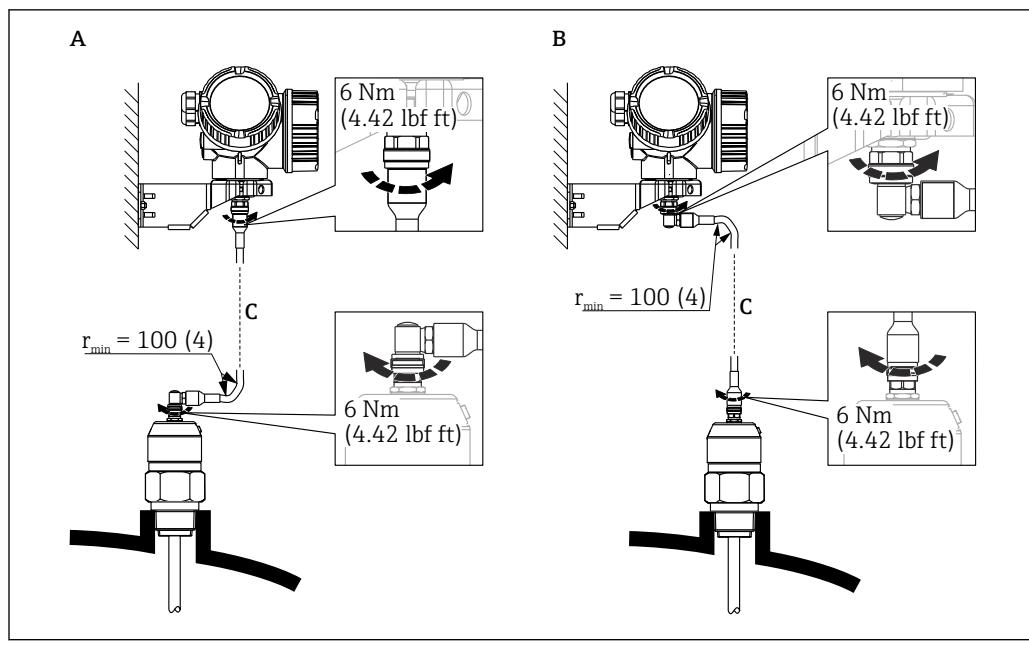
Instalação do invólucro dos componentes eletrônicos usando o suporte de montagem; dimensões: mm (pol.)
